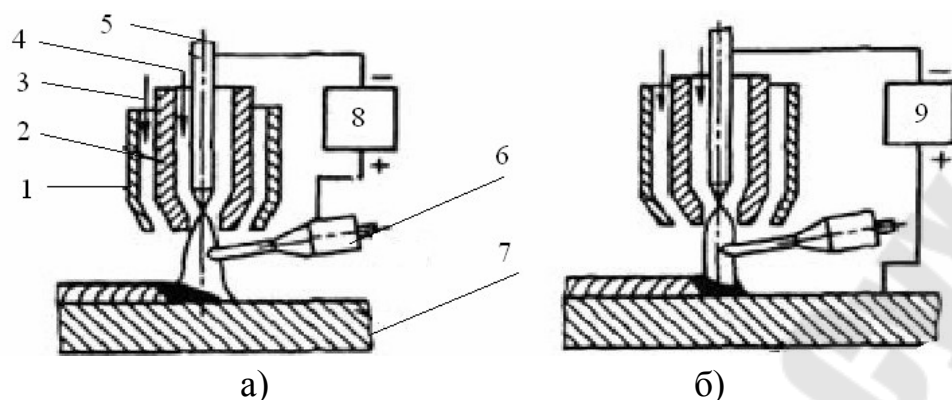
Схемы плазменной наплавки: а – плазменной струей с токоведущей присадочной проволокой; б – плазменной дугой с нейтральной присадочной проволокой; 1 – защитное сопло; 2 – сопло плазмотрона; 3 – защитный газ; 4 – плазмообразующий газ; 5 – электрод; 6 – присадочная проволока; 7 – изделие; 8 – источник питания косвенной дуги; 9 – источник питания дуги прямого действия
